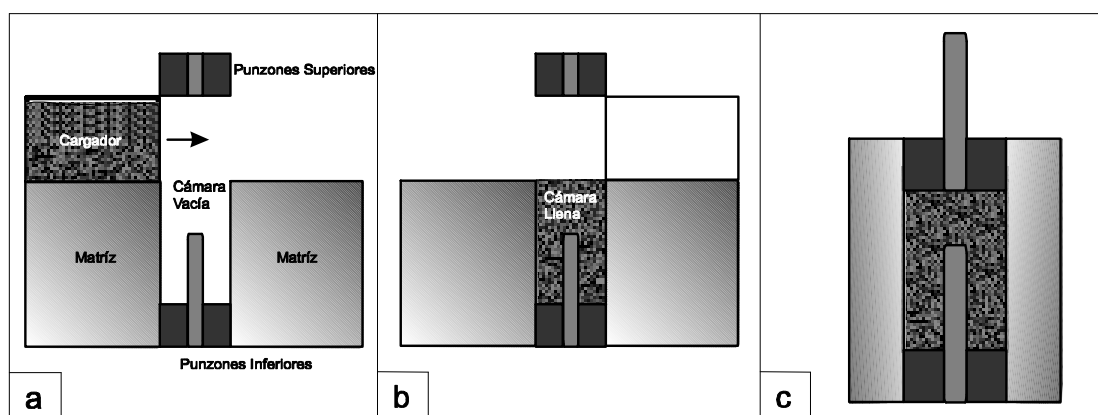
Pieza tipo H, a) llenado de molde, material en el cargador y molde vacío, b) molde totalmente lleno de material, c) transporte de cámara (estado inicial)
